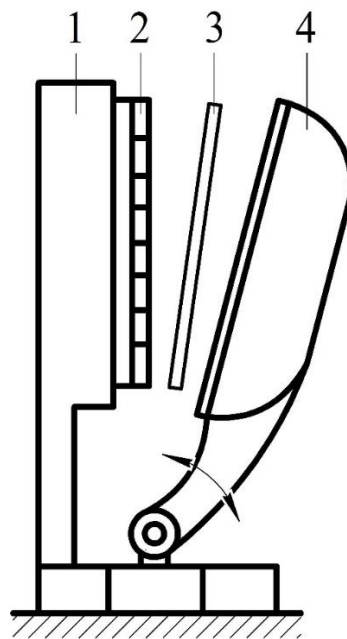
Графічна схема тигельного висікального пресу, 1 – нерухома станина; 2 – висікальна форма; 3 – заготовка палітурного матеріалу; 4 – коливальний тигель
